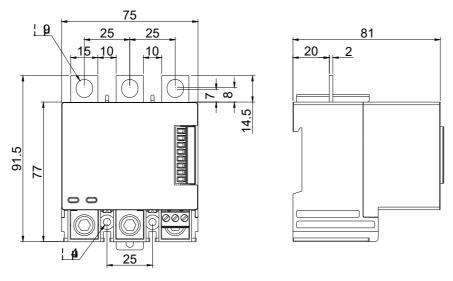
Внешний вид и габаритные размеры КСМ-М4-63
